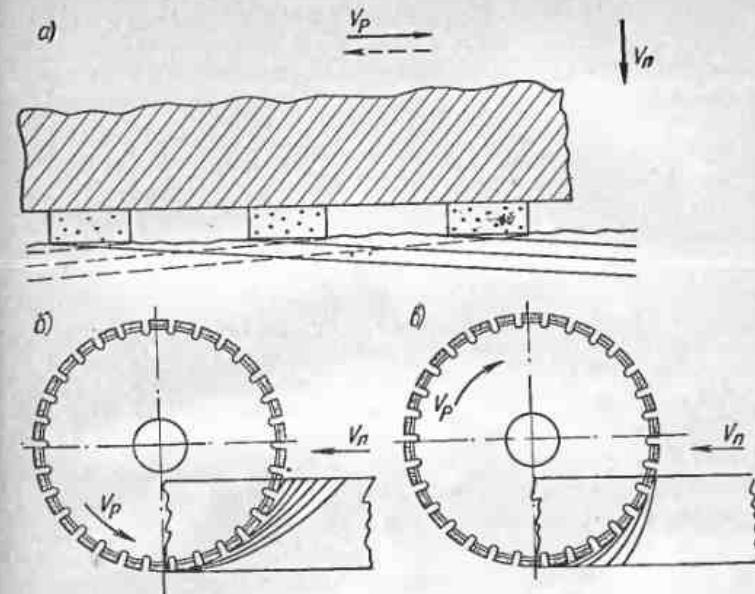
Схемы основных формообразующих движений инструмента и снятия стружки
